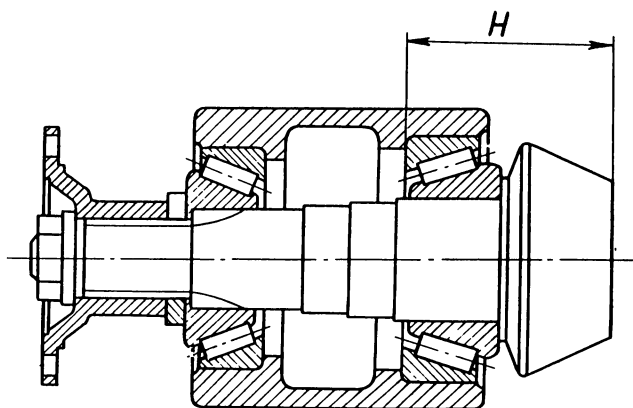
Схема приспособления для определения толщины регулировочной шайбы.
